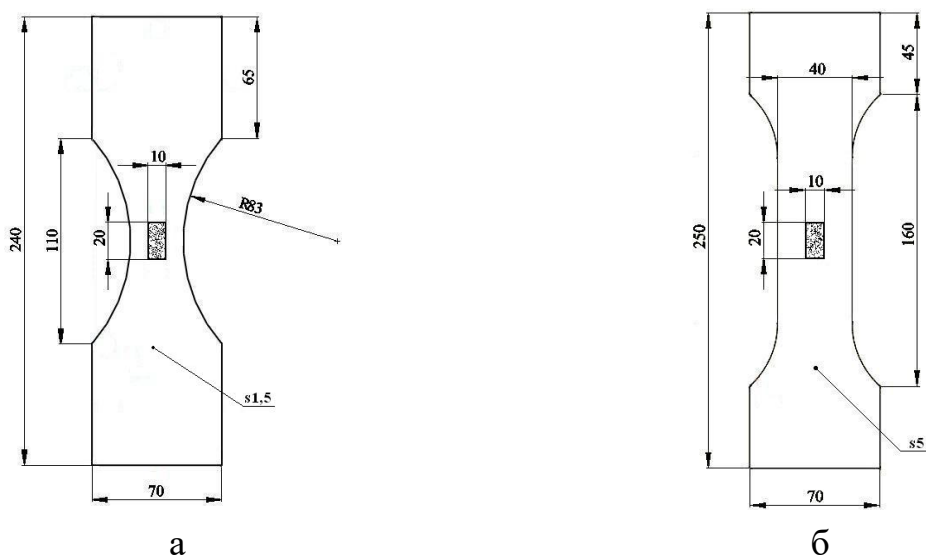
Зразки з фольговими сенсорами втомного пошкодження: а) зразок, виготовлений з сплаву Д16АТ; б) зразок, виготовлений з сплаву 7075Т6 [23]
